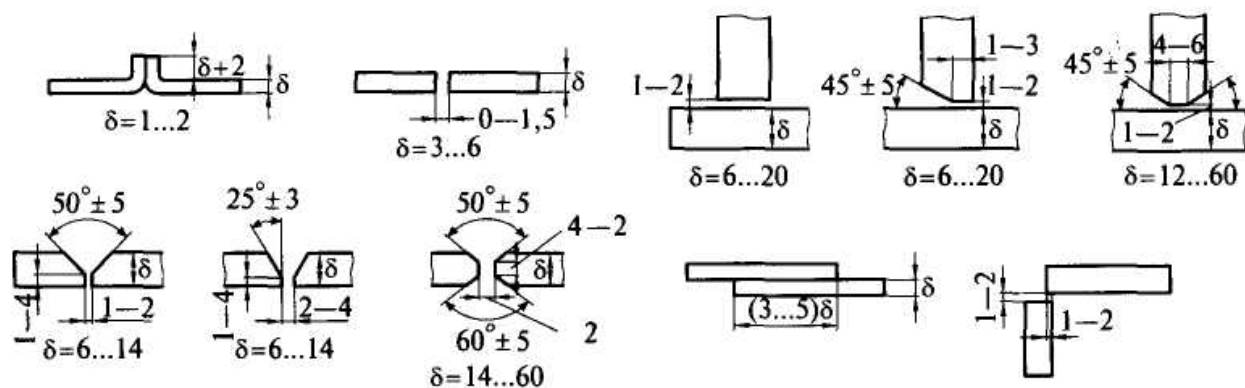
а - Разделка кромок под сварку элементов различной толщины
